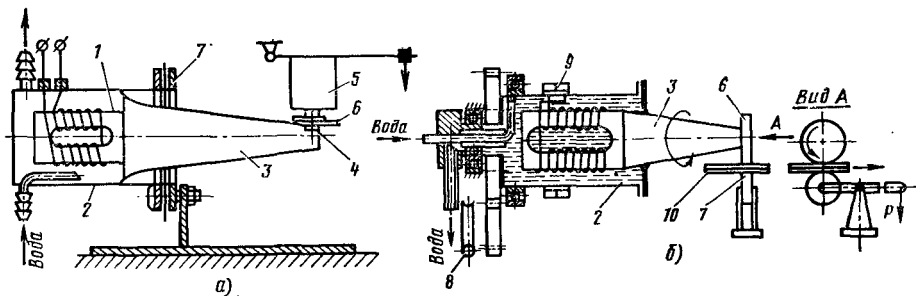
Схема установки для сварки ультразвуком:
